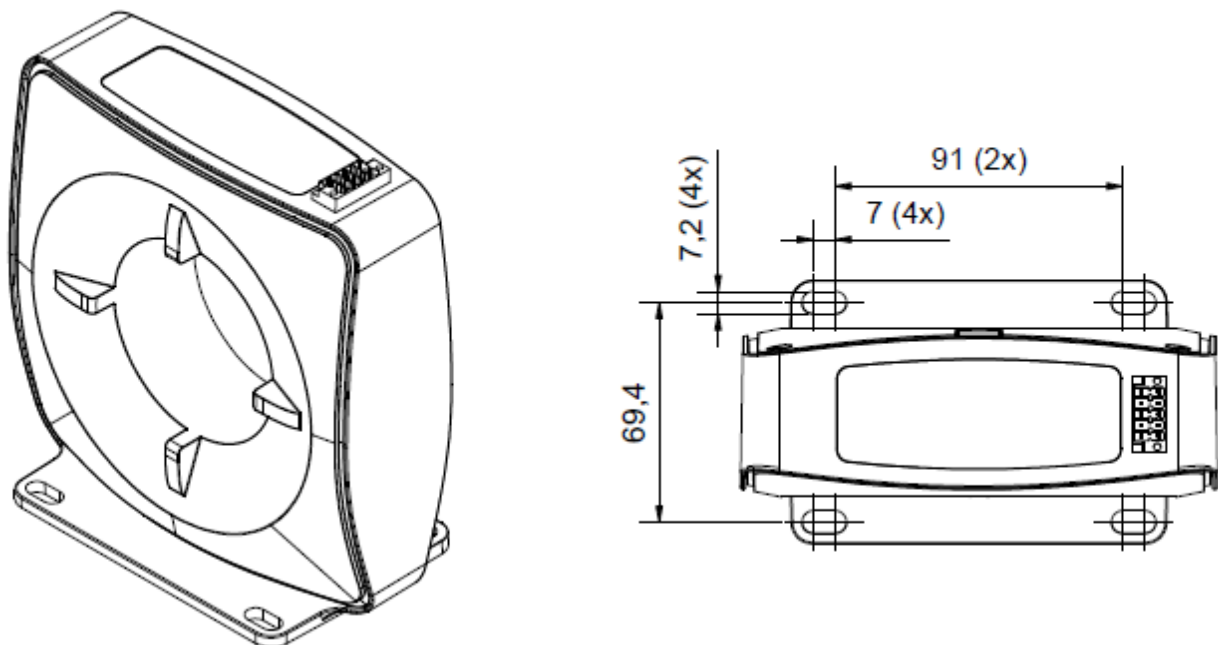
Isometrische Ansicht, Draufsicht; alle Angaben in mm
